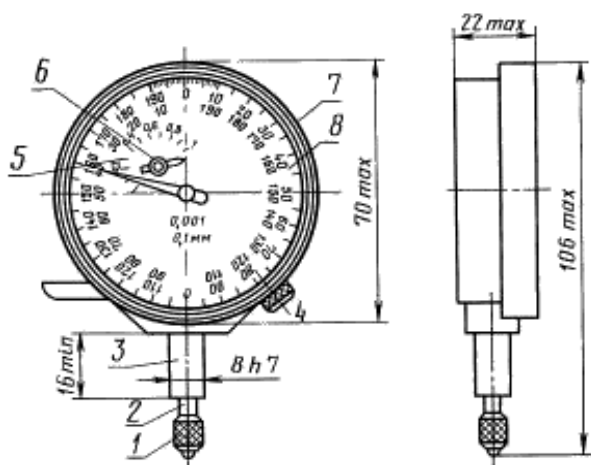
Внешний вид и основные размеры индикаторов типа МИГ:
